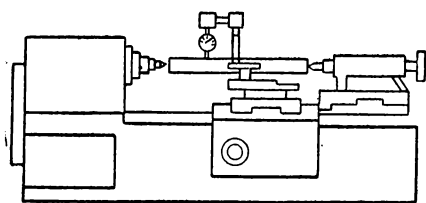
Приспособление для шабрения подшипников шпинделя.
